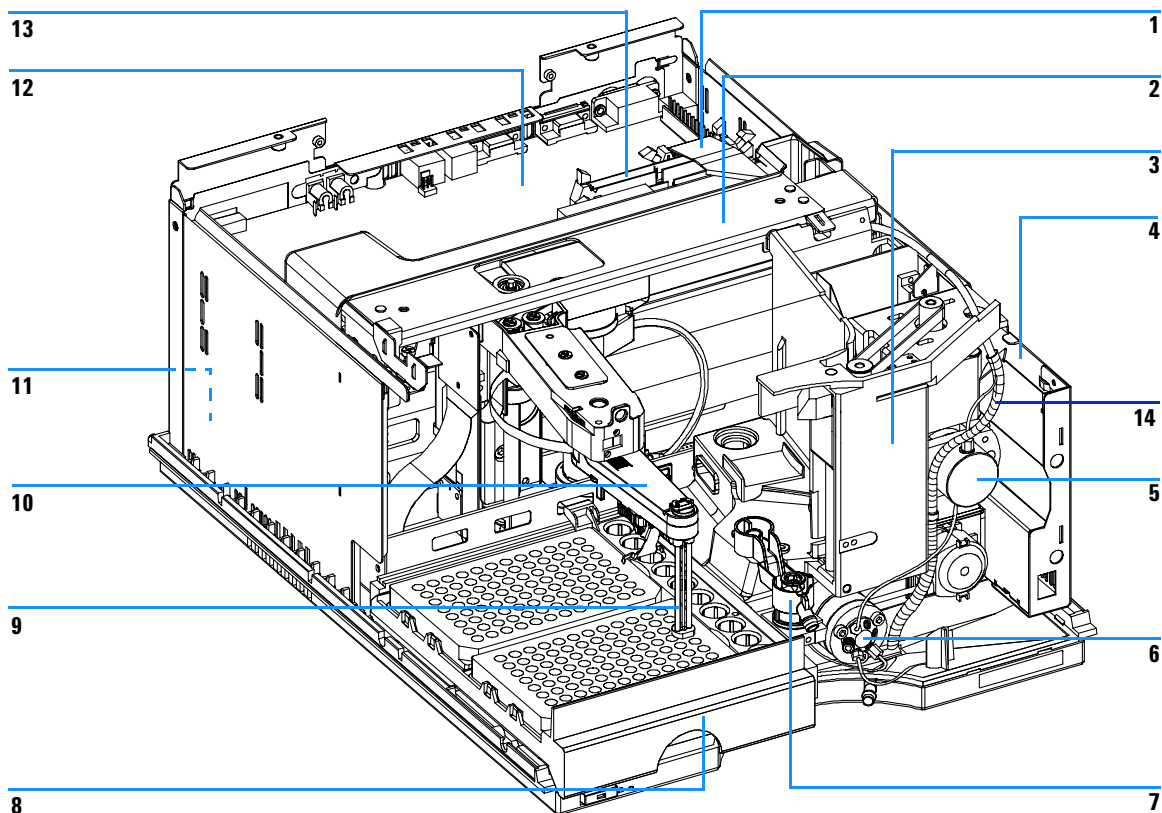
Sous-ensembles principaux du micro-échantillonneur à plaque à puits
